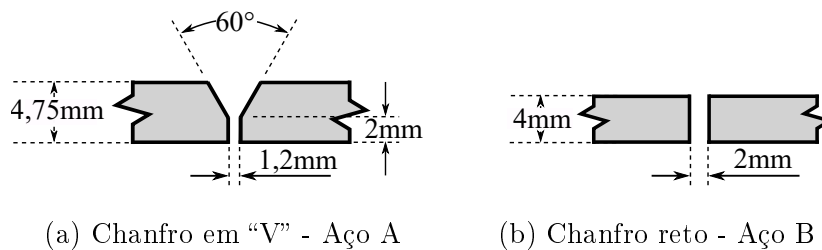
Geometria das juntas soldadas para ambos aços.
